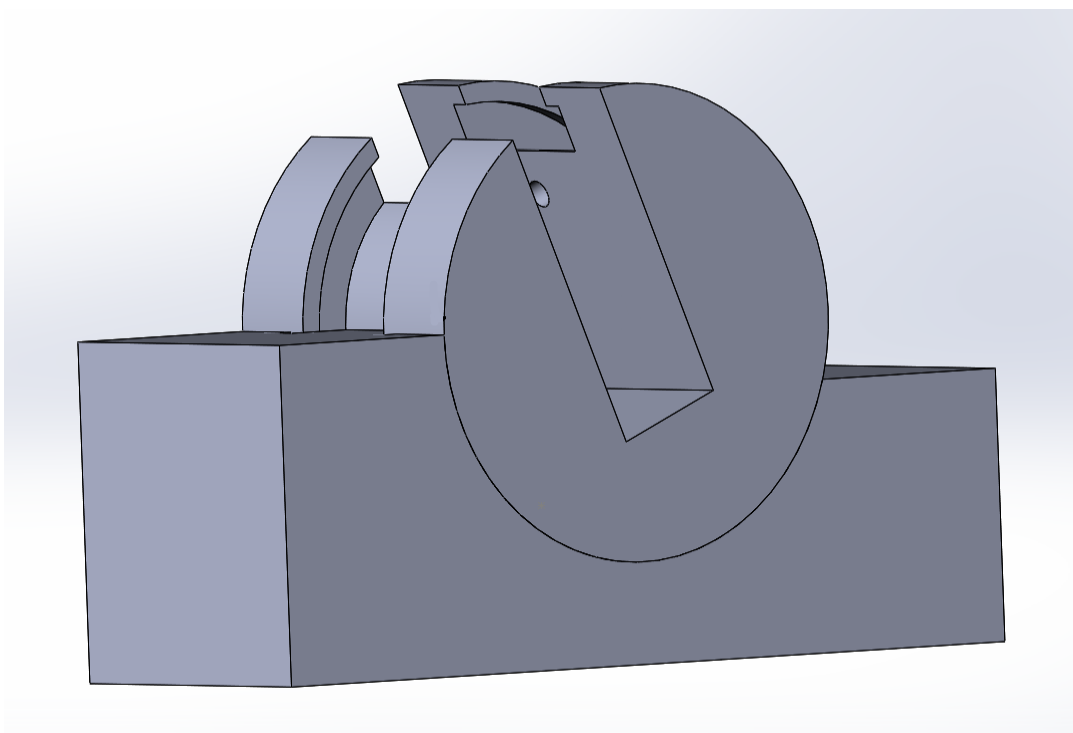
3D модель специального контрольного приспособления для лазерного датчика
